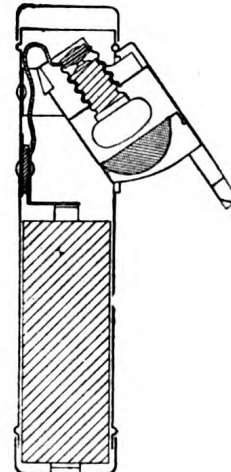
Querschnittsschema der halbgeöffneten Lampe.
